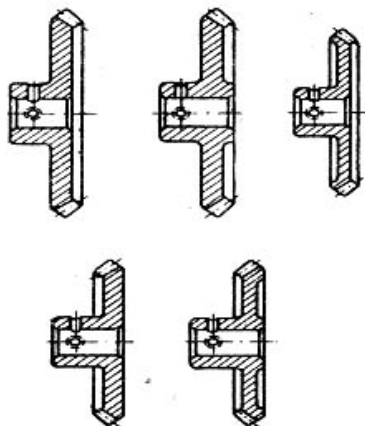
Типовые конструкции конических зубчатых передач
